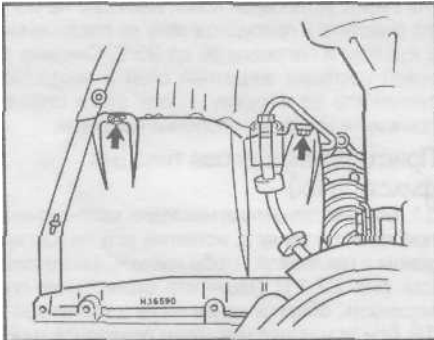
Отверните винты крепления (показаны стрелками) локера арки колеса
